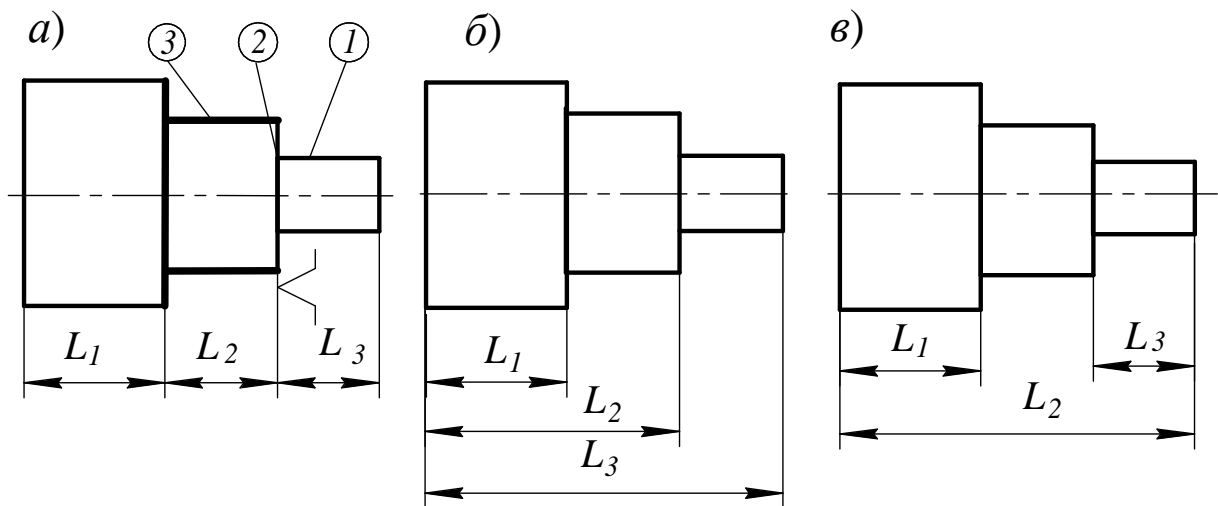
Системы нанесения размеров на чертеже детали цепным (а), координатным (б) и комбинированным (в) способами
